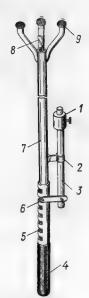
1— груз; 2— зажим; 3— рычаг; 4— ручка; 5— труба с прорезями; 6— вилка; 7— штанга; 8— трос; 9— упор
